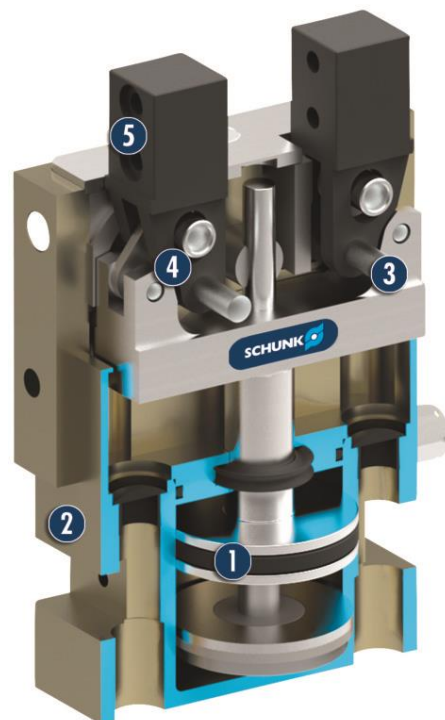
Konstrukce elektrického angulárního chapadla [5]
